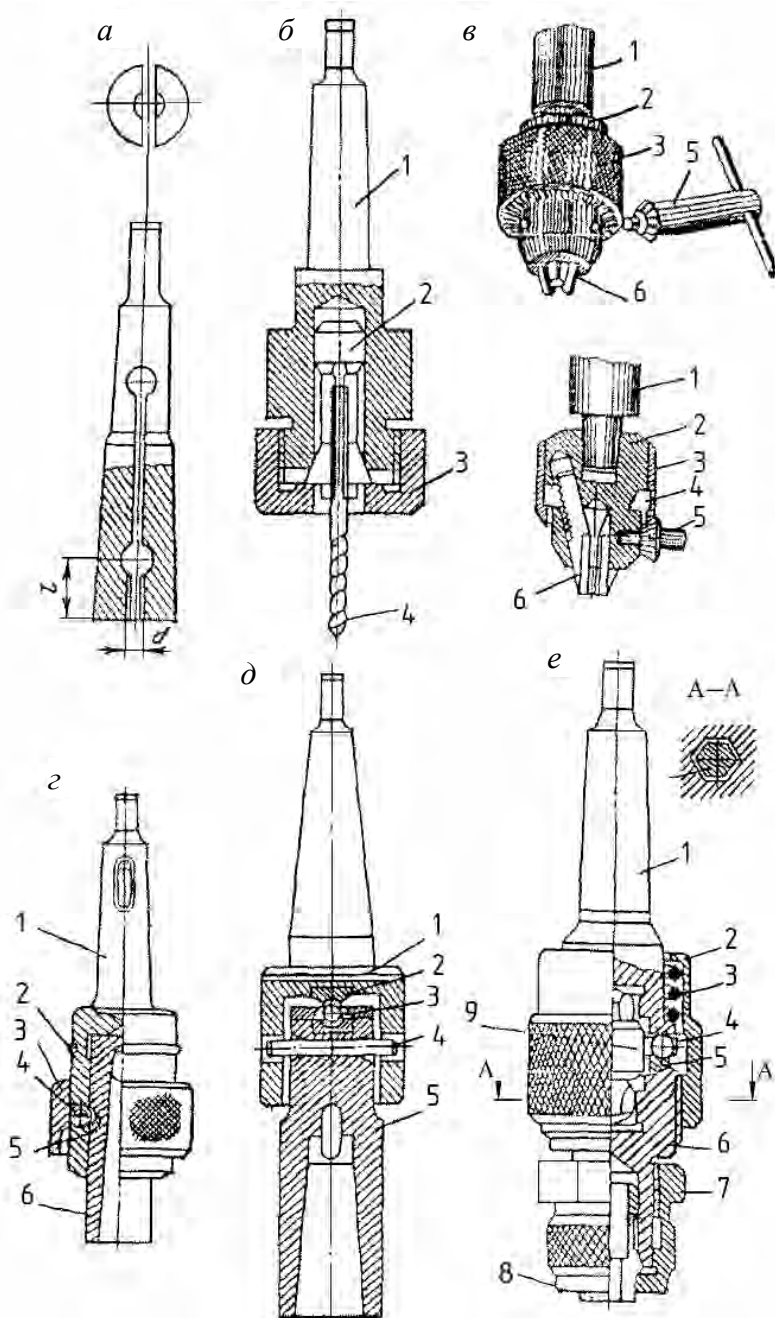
Типовые устройства для крепления осевых инструментов
